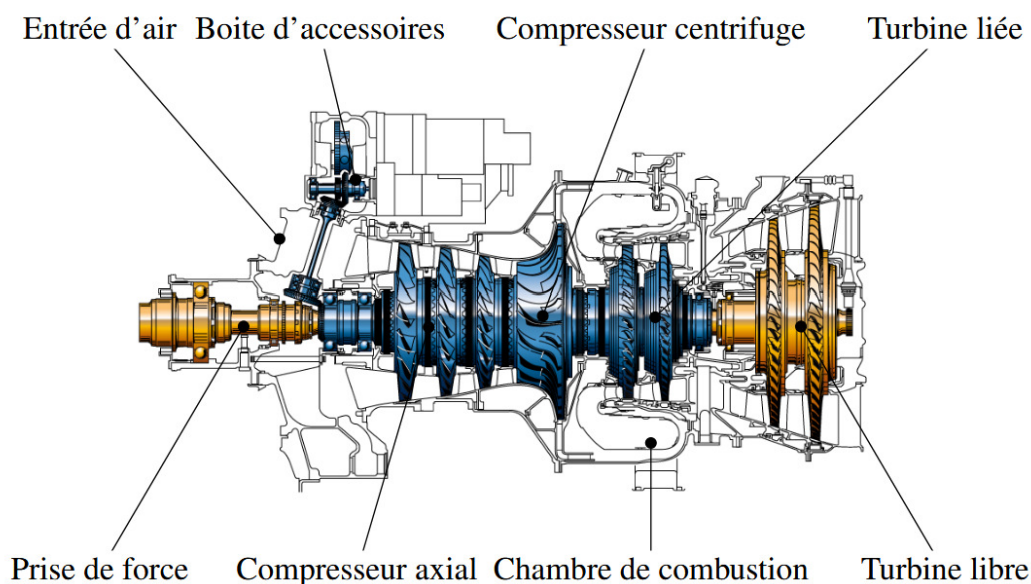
Vue en coupe d'un turbomoteur à turbine libre (Helicopter turboshaft RTM322, Turbomeca-Rolls Royce [4]) de [5].
